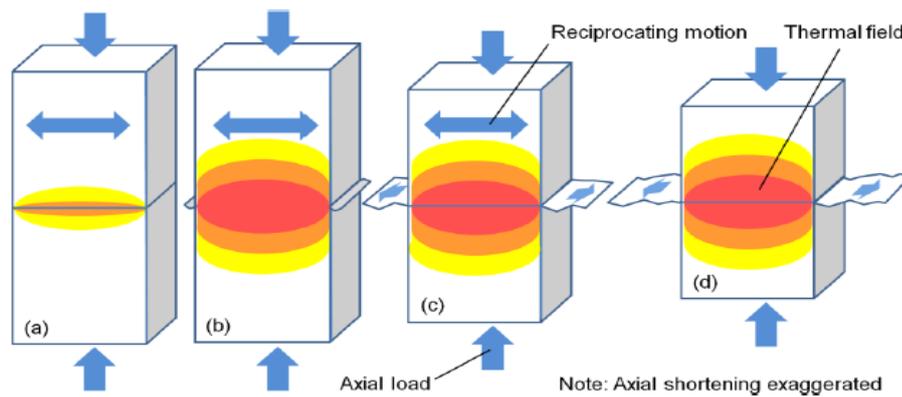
Prinsip *friction stir welding* (Wijayanto, 2012)
